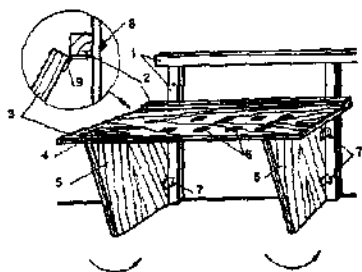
Рабочее место на балконе или лоджии: 1 — конструкция ограждения балкона или лоджии; 2 — опорный брусок; 3 — подвесная доска; 4 — передний упор; 5 — поворотная опорная доска; 6 — гнезда для заднего упора; 7 — металлическая петля; 8 — крепежный болт; 9 — металлическая лента-петля (рояльная петля)
